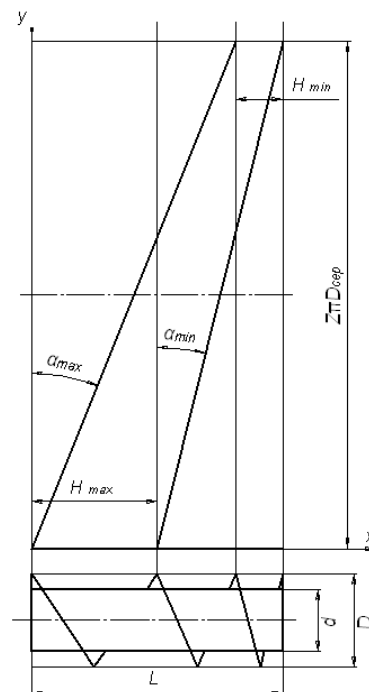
Розгортка гвинтової канавки шнека м'ясорубки
